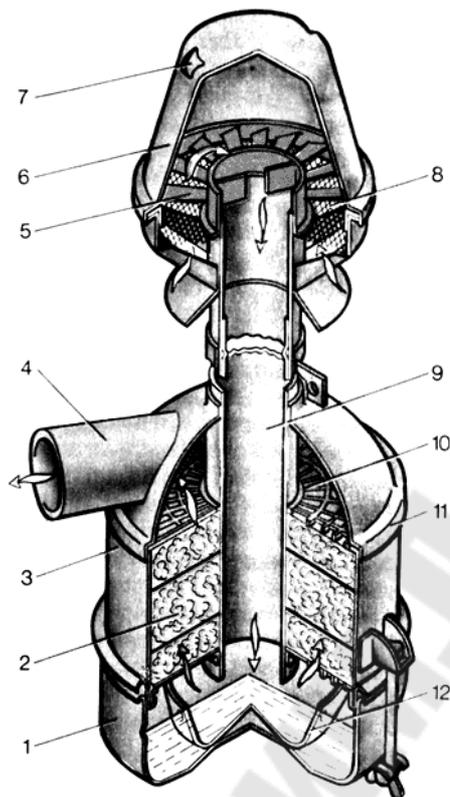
Трехступенчатый воздухоочиститель двигателя Д–240: 1 – поддон, 2 – фильтрующие элементы (из капроновой путанки), 3 – корпус, 4 – выходной патрубок, 5 – завихритель, 6 – инерционный очиститель, 7 – окно для удаления пыли, 8 – сетка, 9 – трубка, 10 – опорная обойма, 11 – головка, 12 – масляная ванна для направления потока воздуха и масла.
